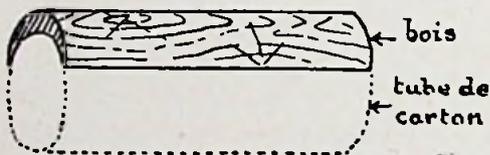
La pièce de bois rapportée sur le dessus de la bobine.
